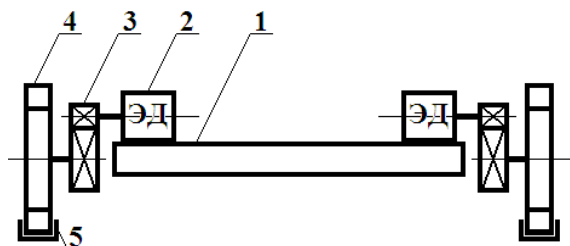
Конструкция мостового агрегата: 1 - несущая ферма для крепления сельхозорудия; 2 - электродвигатель; 3 - редуктор; 4 - колесо; 5 - направляющая колея.
